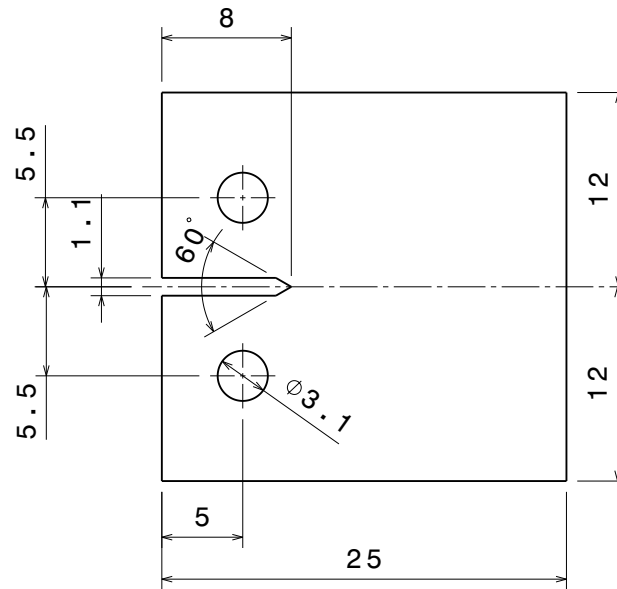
Geometría y dimensiones (mm) de la probeta C(T) de aluminio utilizadas para crecimiento de grieta y DIC.
